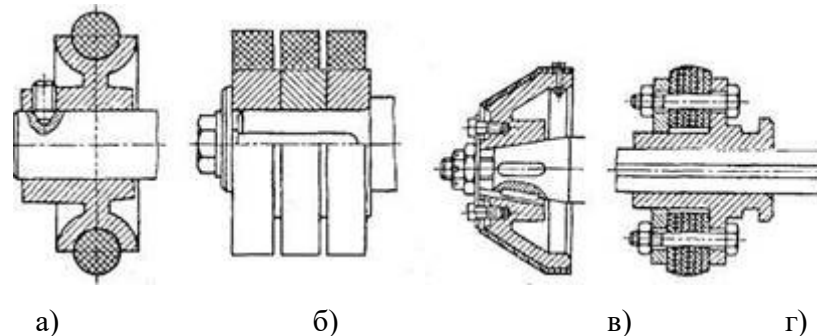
Материалы трущихся поверхностей катков: а, б – резина; в – фибра; г – кожа
